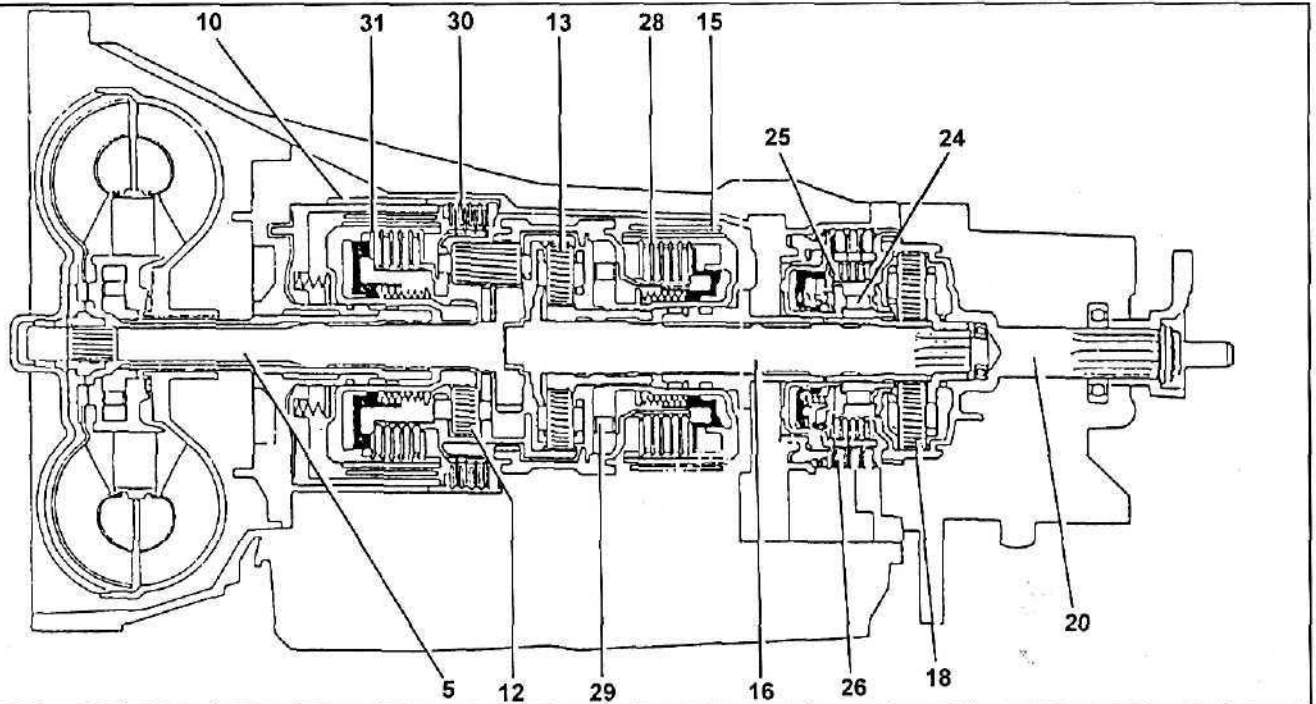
Автоматическая коробка передач 722.5. 5 - Ведущий вал, 10 - Ленточный тормоз В1, 12 - Планетарный ряд со сцепленными сателлитами, 13 - Средний планетарный ряд, 15 - Ленточный тормоз В2, 16 - Промежуточный вал, 18 - Повышающий планетарный ряд, 20 - Ведомый вал, 24 - Муфта свободного хода F2, 25 - Блокировочная муфта KS, 26 - Дисковый тормоз BS, 28 - Блокировочная муфта K2, 29 - Муфта свободного хода F1, 30 - Дисковый тормоз В3, 31 - Блокировочная муфта K1.
